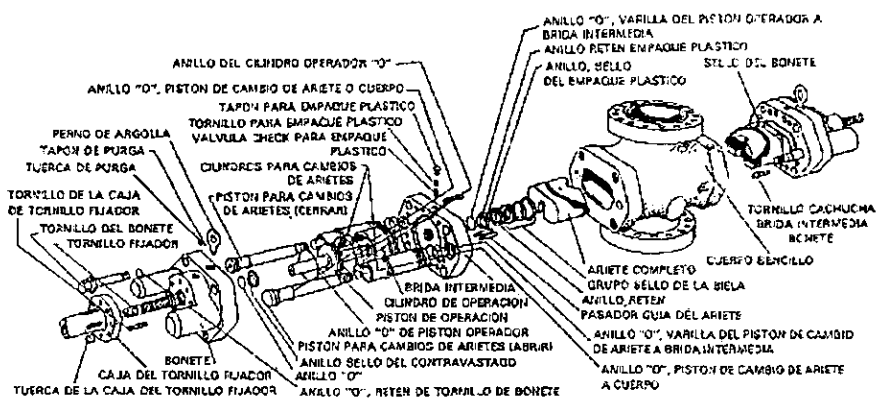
Partes componentes del preventor de arietes CAMERON tipo "U"
